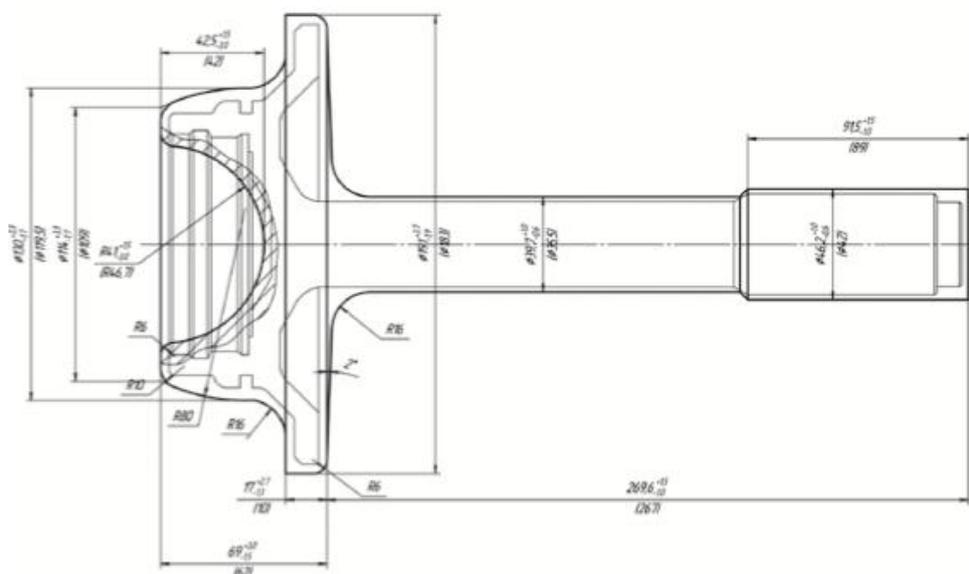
Чертеж поковки «вал торсионный», изготовленной по предложенной ресурсосберегающей технологии
